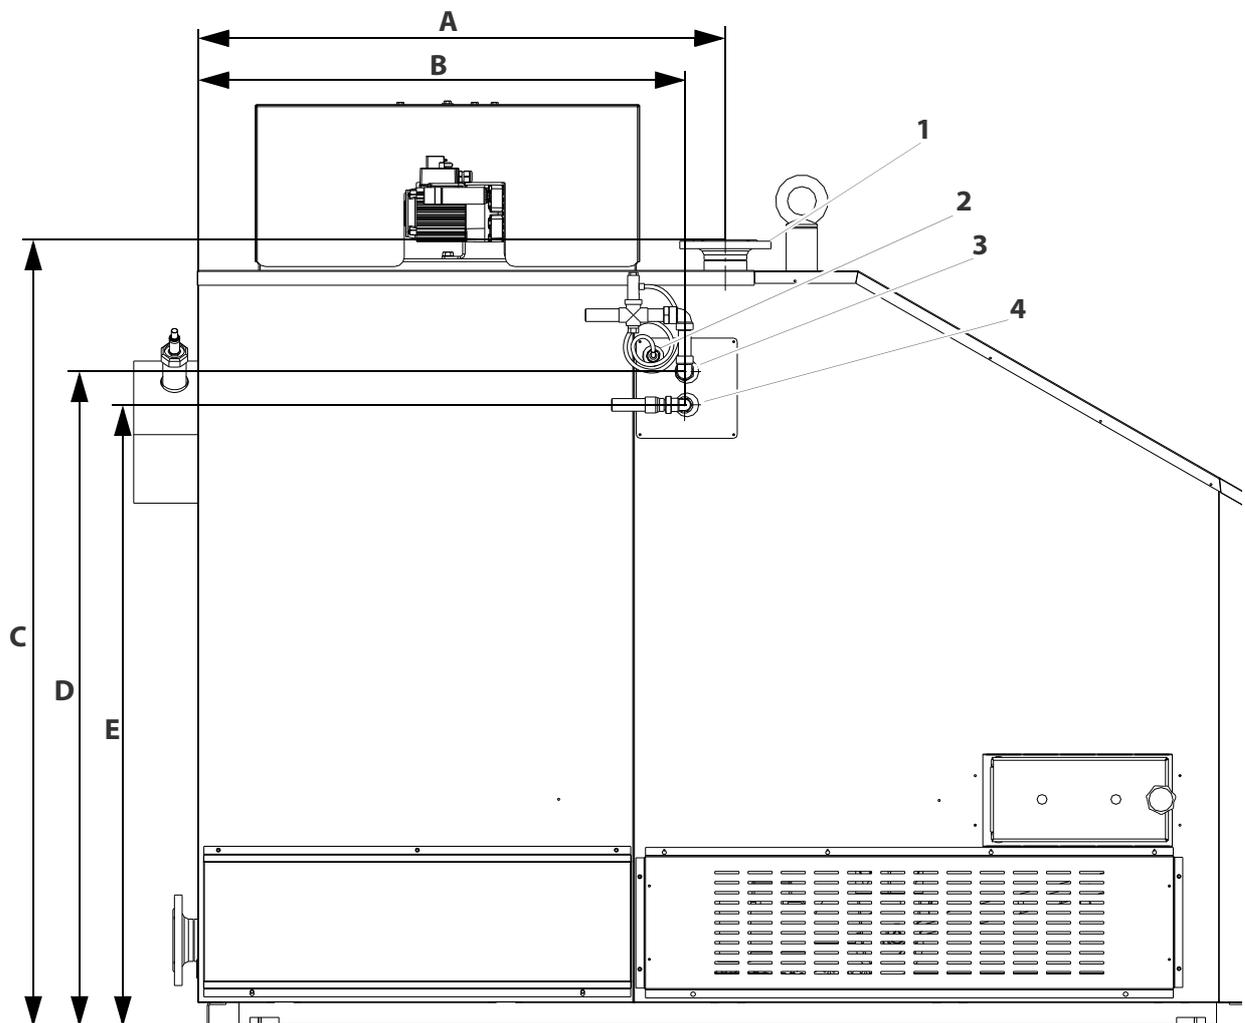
/6 - Dimensions face arrière - HDG Compact 150/200
